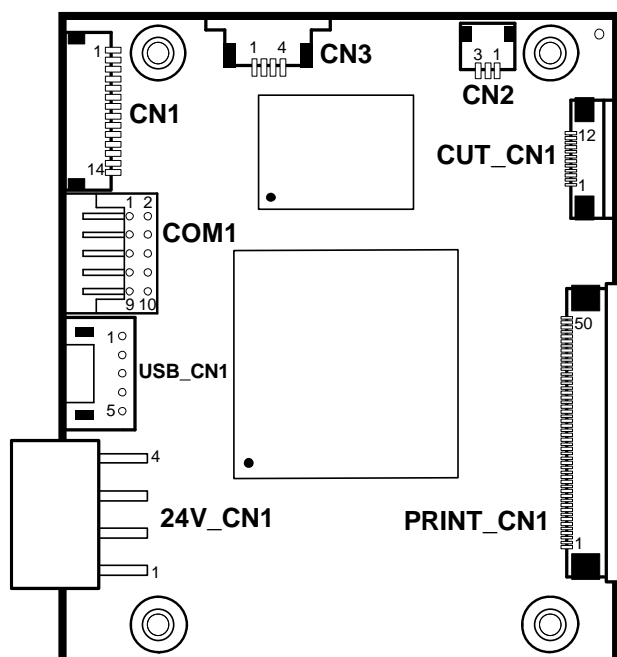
Localizações dos componentes da placa de impressora MB-1030
